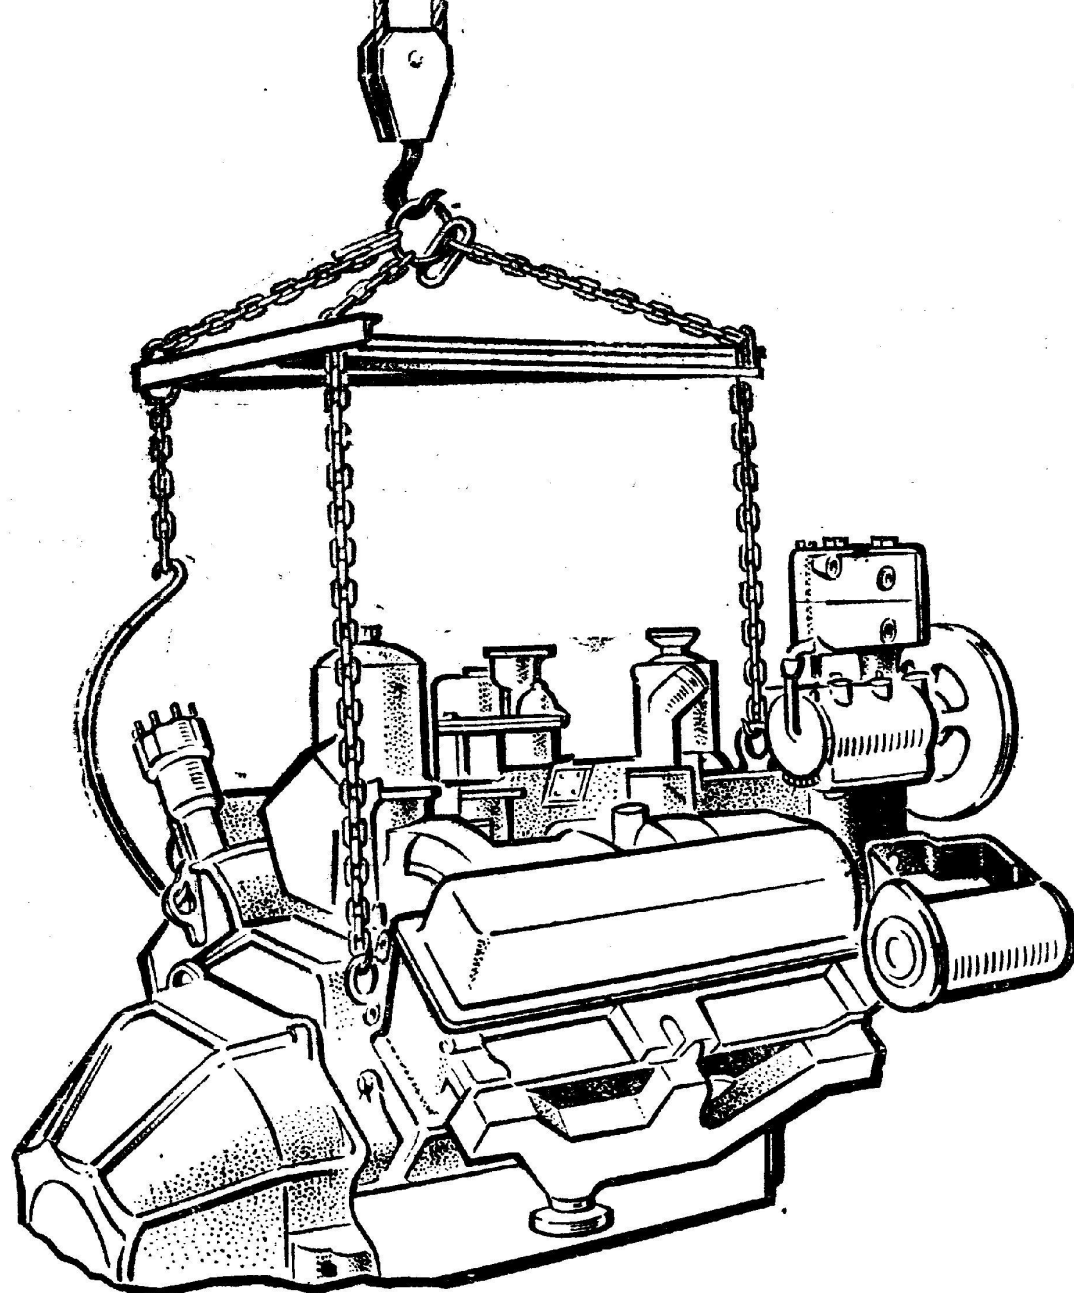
Приспособление для закрепления двигателя ЗИЛ-130 к крюку подъемно-транспортного оборудования
